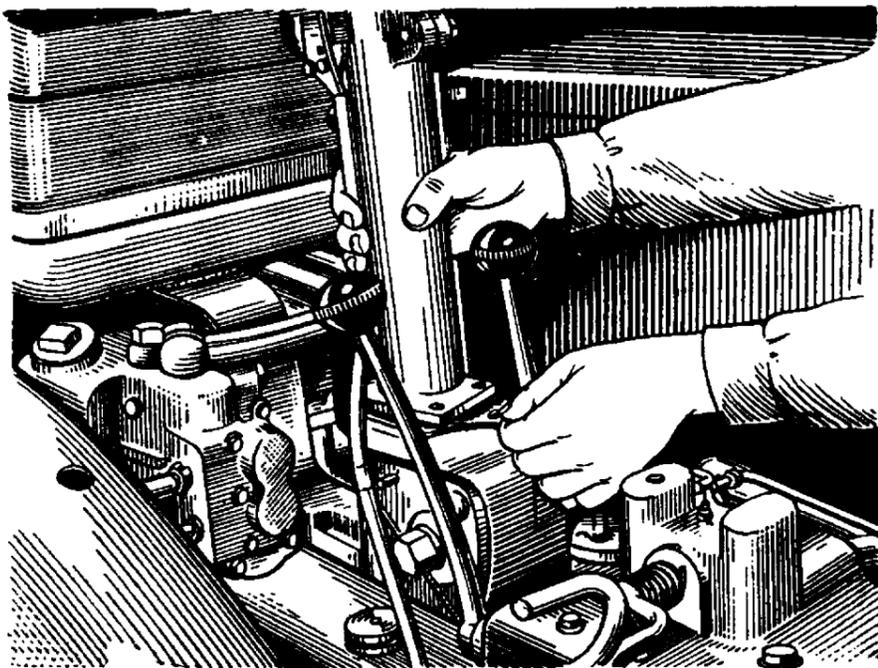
Регулировка осевого зазора конических подшипников рулевого управления.
